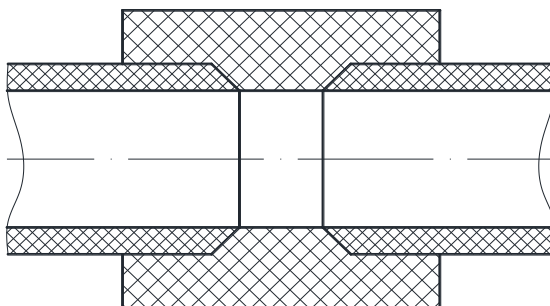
Конструктивные элементы шва сварного соединения (шов НС1)
